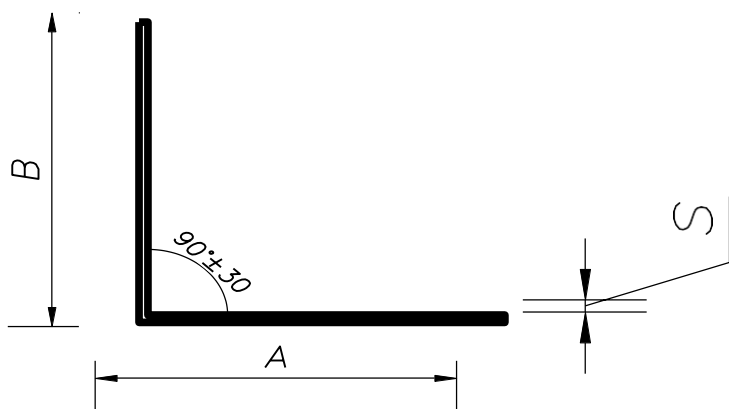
Профиль Г-образный горизонтальный (ПГГ).
